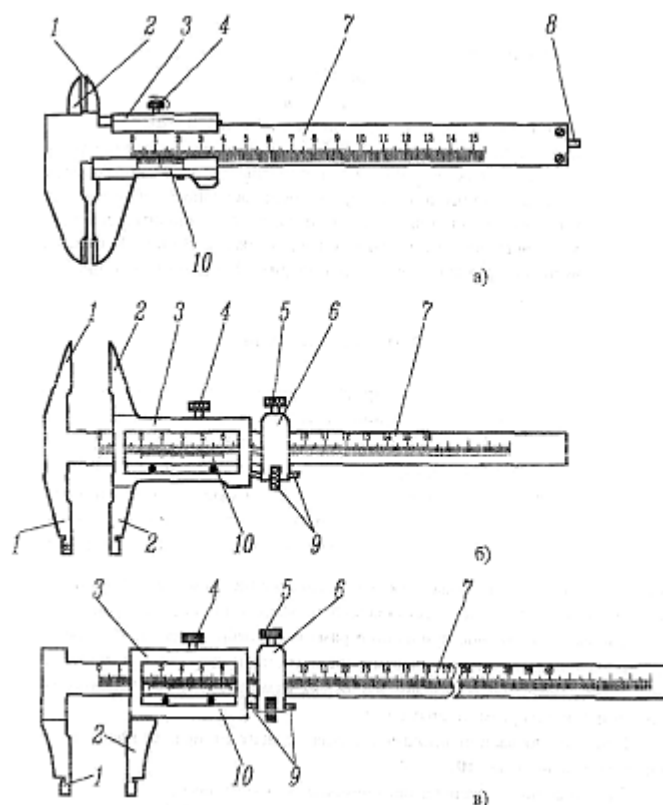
Штангенциркули: а - ШЦ I; б – ШЦ II; в - ШЦ III; 1 - неподвижные губки; 2 – подвижные губки; 3 - рамка; 4 - зажим рамки; 5 - зажим рамки микрометрической подачи; 6 - рамка микрометрической подачи; 7 - штанга; 8 - линейка глубиномера, 9 - винт и гайка микрометрической подачи; 10 – нониус
